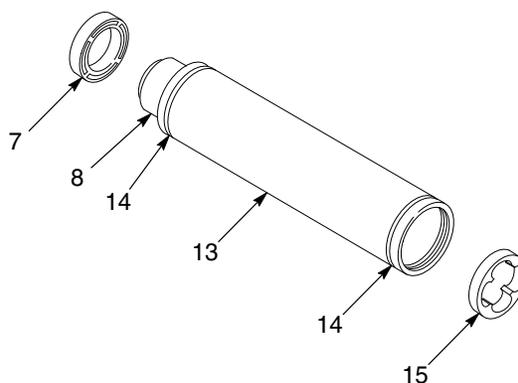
Zestaw serwisowy modułu ładującego
